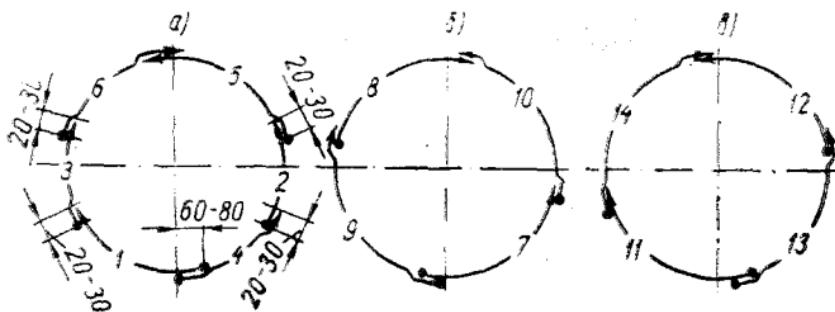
Схема сварки стыков труб диаметром 400 мм
